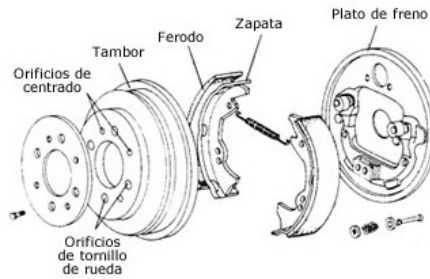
Conjunto de tambor-rueda montado [6]s.
